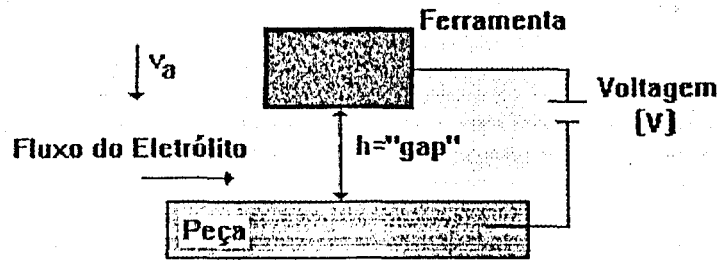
Esquema que simboliza o avanço da ferramenta em uma operação de usinagem eletroquímica.
